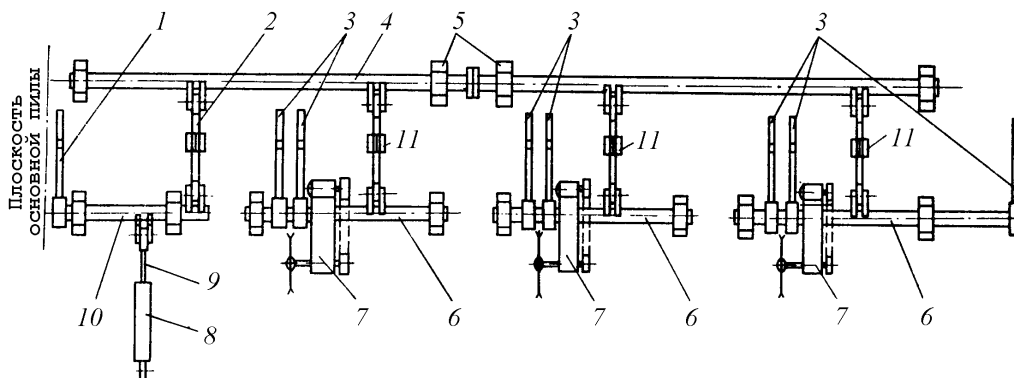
Схема привода механизма подачи пильного блока установки ЛО-15С
